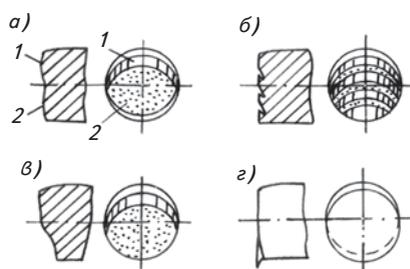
Неоднородности и возможные дефекты на торцах заготовок, отрезанных сдвигом: а, б — неоднородность поверхности; в — несколько гладких поясков; з — ступенчатый торец;
